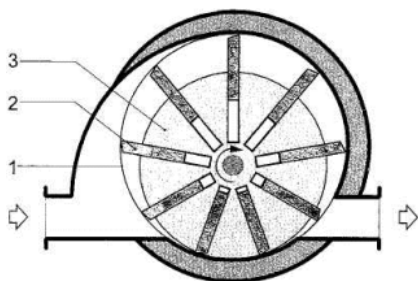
Пластинчатый (шиберный) компрессор:
